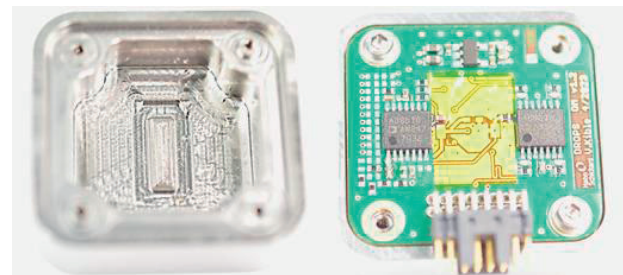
Innenansicht Gehäuse (links) und montierter Demonstrator (rechts)
